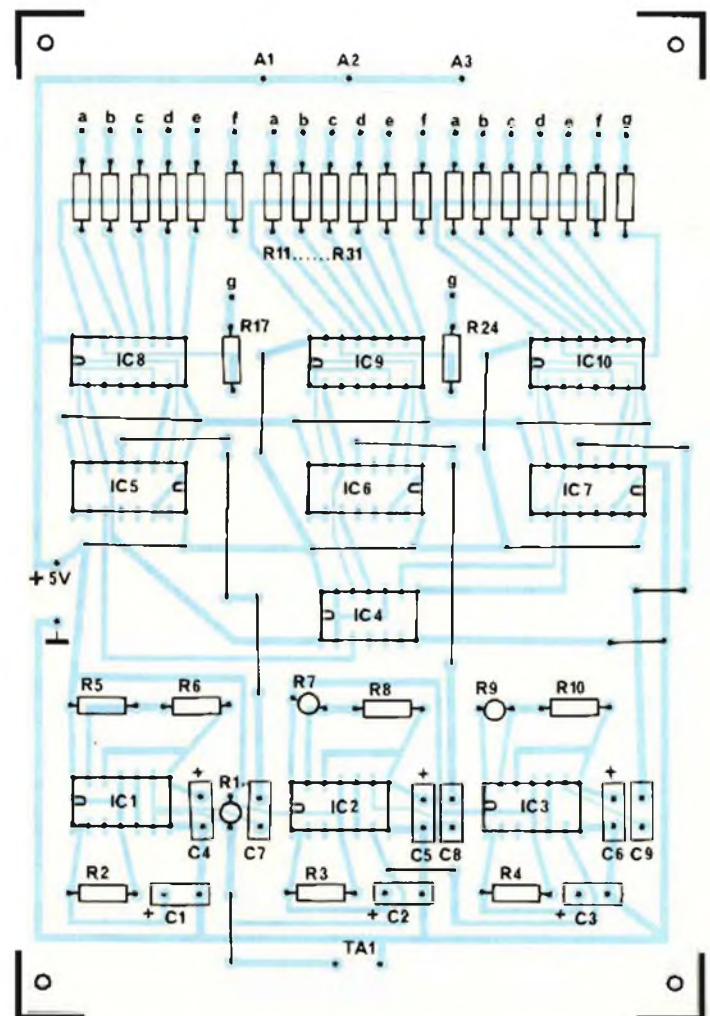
Circuito stampato lato componenti. Si notino i ponticelli da eseguire per completare il circuito.
